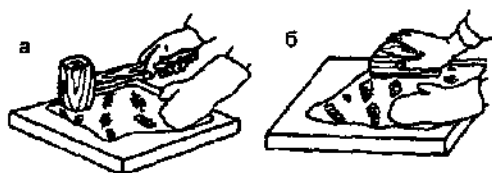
Правка тонкого листового металла: а — киянкой; б — деревянным или металлическим бруском
